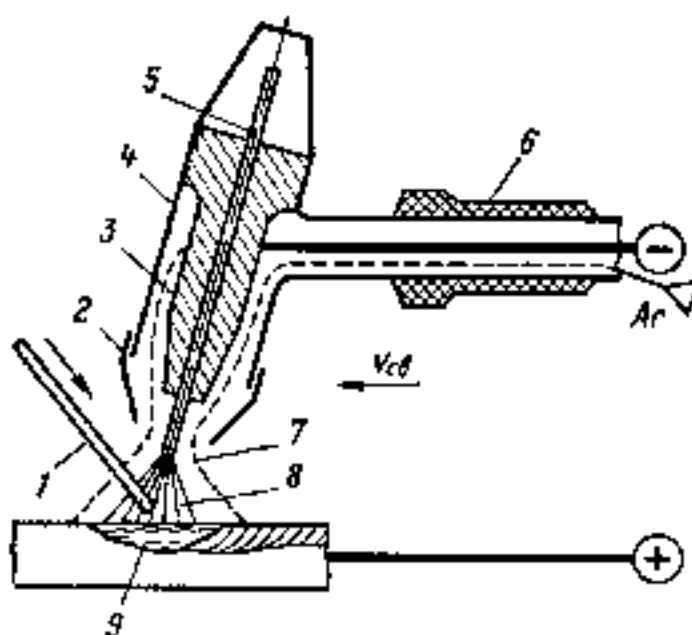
Схема аргодуговой сварки стали вольфрамовым электродом: 1 – присадочный стальной пруток или проволока, 2 – сопло; 3 – окоподводящий мундштук; 4 – корпус горелки; 5 – плавящийся вольфрамовый электрод; 6 – рукоятка горелки; 7 – атмосфера аргона; 8 – сварочная дуга; 9 – ванна расплавленного металла
